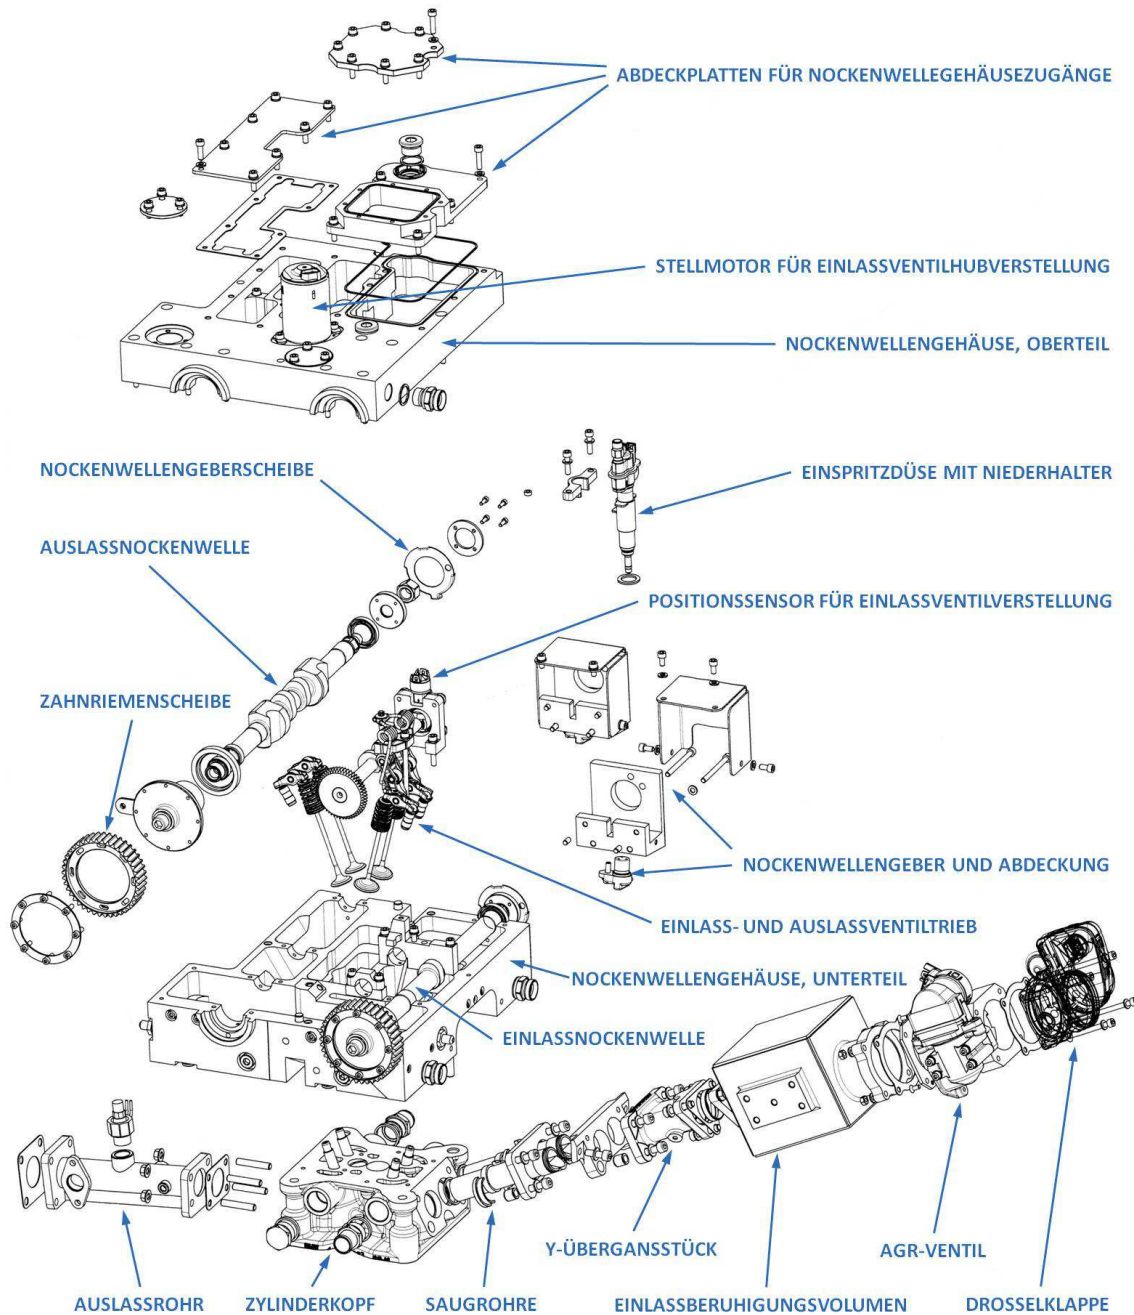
Explosionszeichnung von Nockenwellengehäuse und Zylinderkopf
